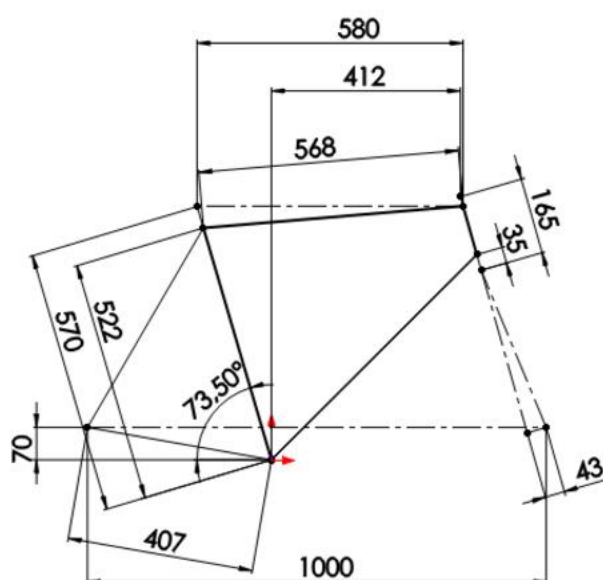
Disseny lineal inicial del quadre amb cotes en mil·límetres (mm)
